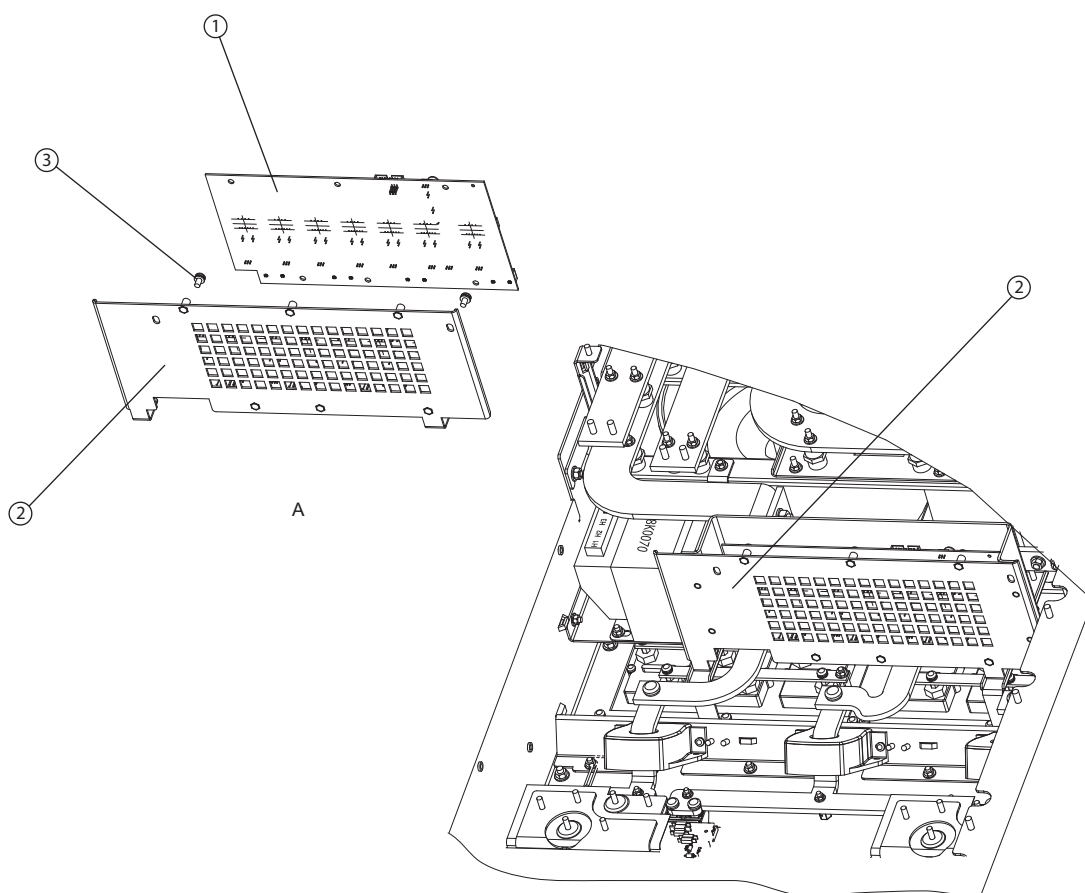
Placa de Montagem do Terminal de Entrada
